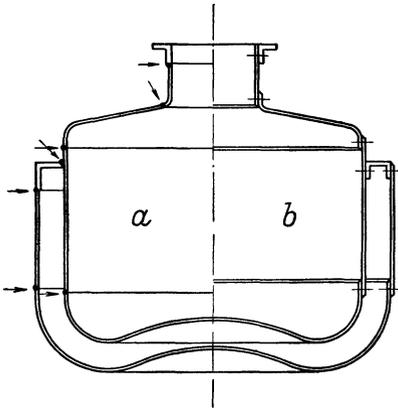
Kochkessel, geschweißt und genietet.
